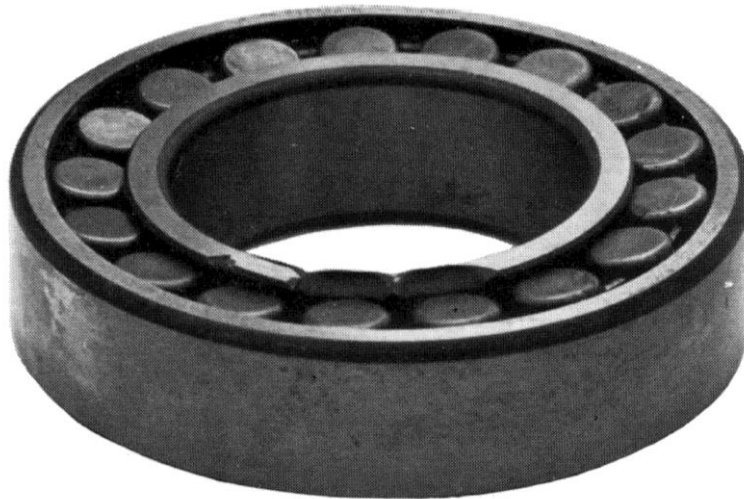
rotura del borde de una pista por percusión durante el montaje [3].
